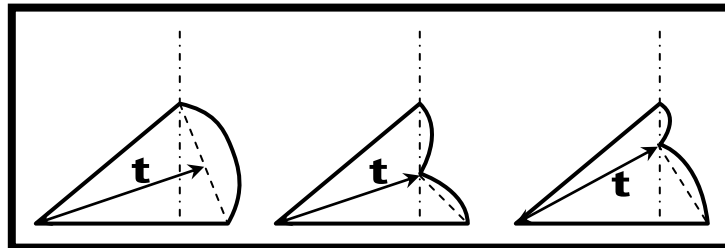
Área efectiva sobre una soldadura de filete.
